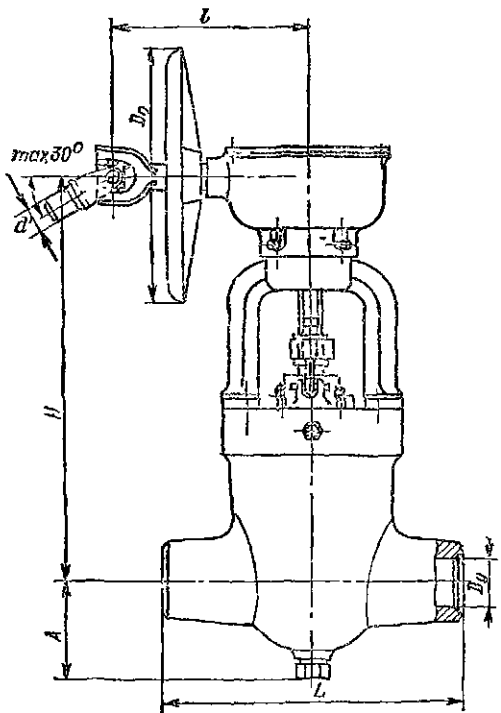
Задвижки ЧЗЭМ с маховиком, шарнирной муфтой и конической зубчатой передачей
